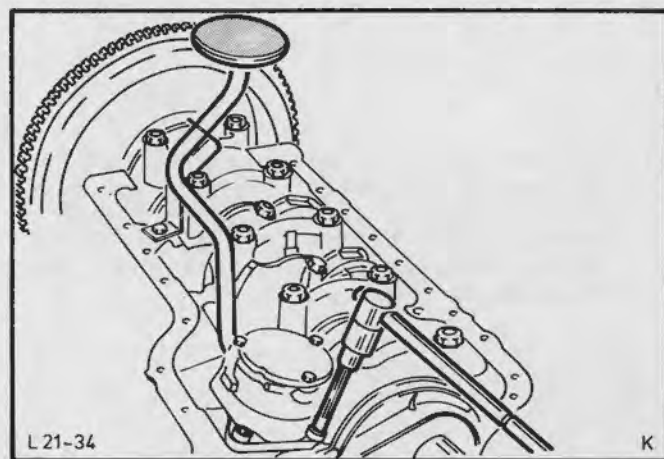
Afmonter olie-pumpen med specialværktøj 21-012
